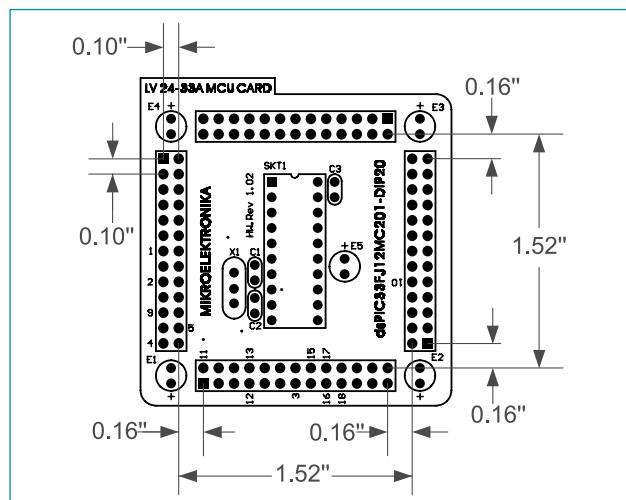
Dimensiones de la tarjeta MCU para la *MCU Card 10
